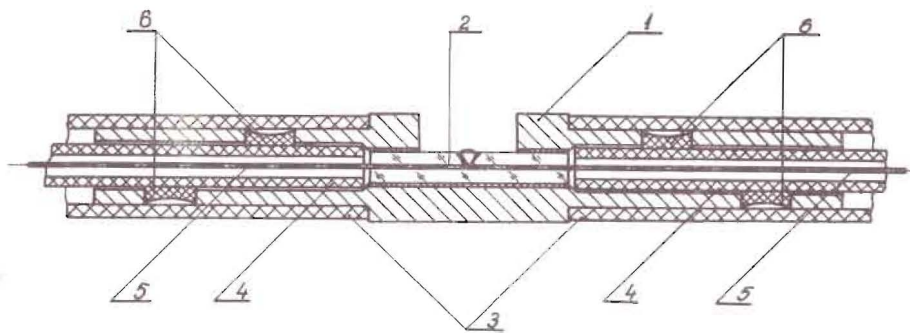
Неразъемный соединитель для сращивания кабелей ВОЛС с помощью прецизионной втулки: 1 - корпус; 2 - прецизионная втулка /капилляр/; 3 - резиновый наконечник; 4 - оболочка кабеля; 5 - световод; 6 - паз для клея.
